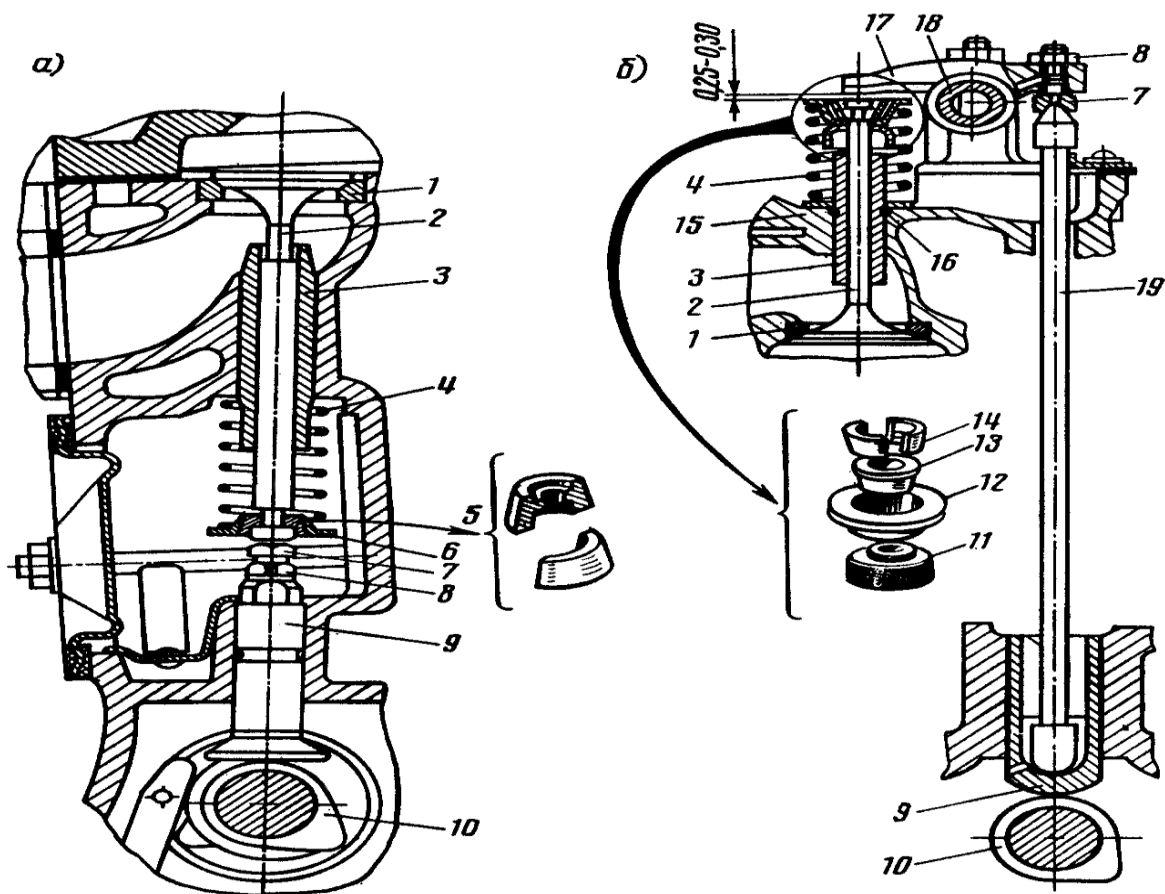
Схемы газораспределительных механизмов с нижним (а) и верхним (б) расположением клапанов: 1 – седло; 2 – клапан; 3 – направляющая втулка; 4 – пружина; 5 и 14 – сухарики; 6 и 12 – тарелки; 7 – регулировочный болт; 8 – контргайка; 9 – толкатель; 10 – кулачок распределительного вала; 11 – маслоотражательный колпачок; 13 – втулка; 15 – головка цилиндров; 16 – стопорное кольцо; 17 – коромысло; 18 – ось коромысла; 19 – штанга
